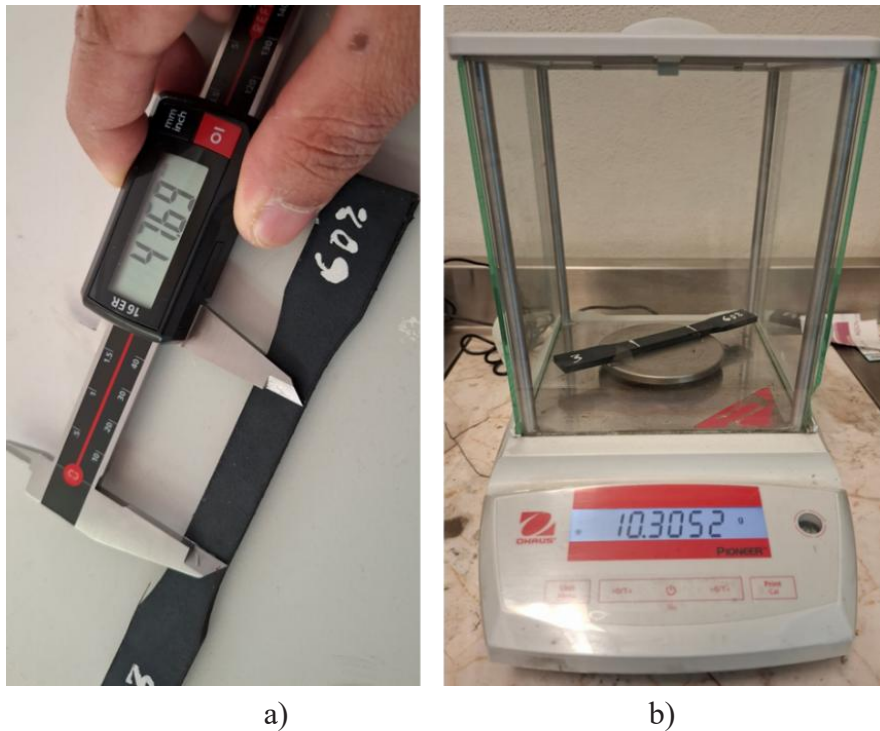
Medición de: a) dimensiones; y b) la masa de las probetas fabricadas.
